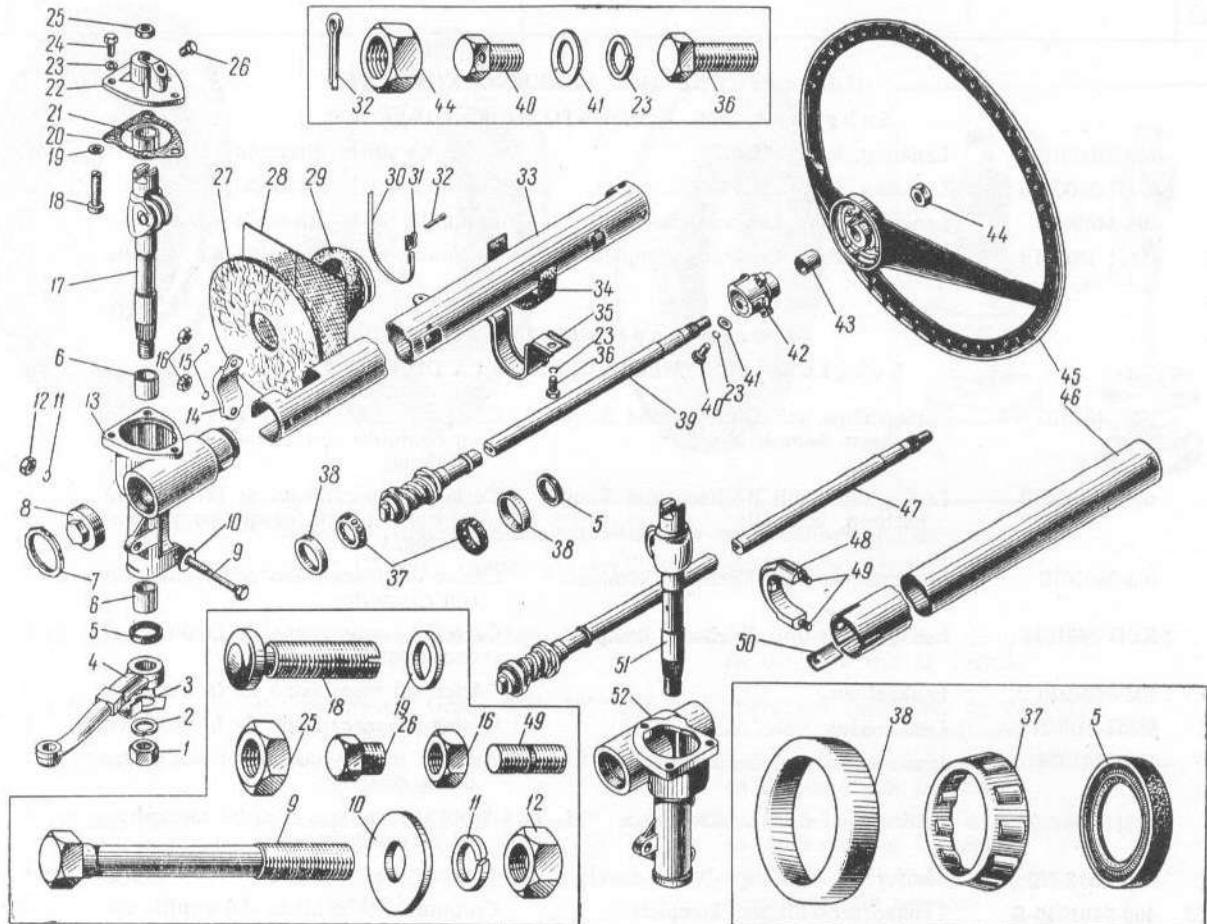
Lenksäule mit Teilen zur Befestigung am Fahrzeug
